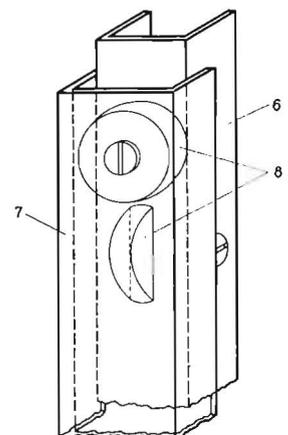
Rollenführung des Meßrahmens für die senkrechte Kraftkomponente
